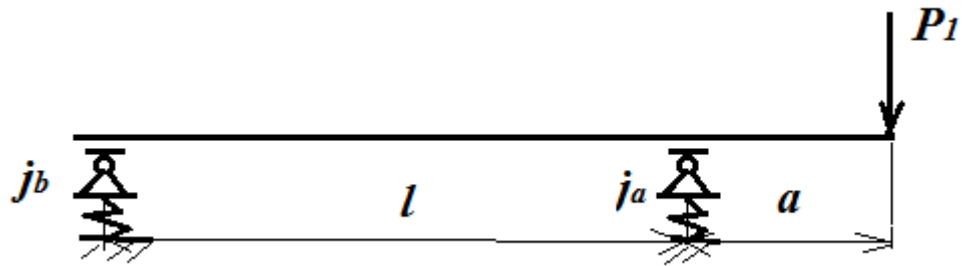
Схема шпindelного вузла із пружними опорами
